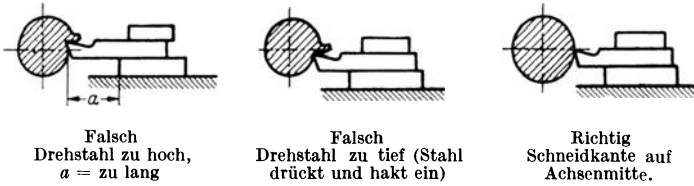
Das Einspannen der Maschinendrehstäbe.
